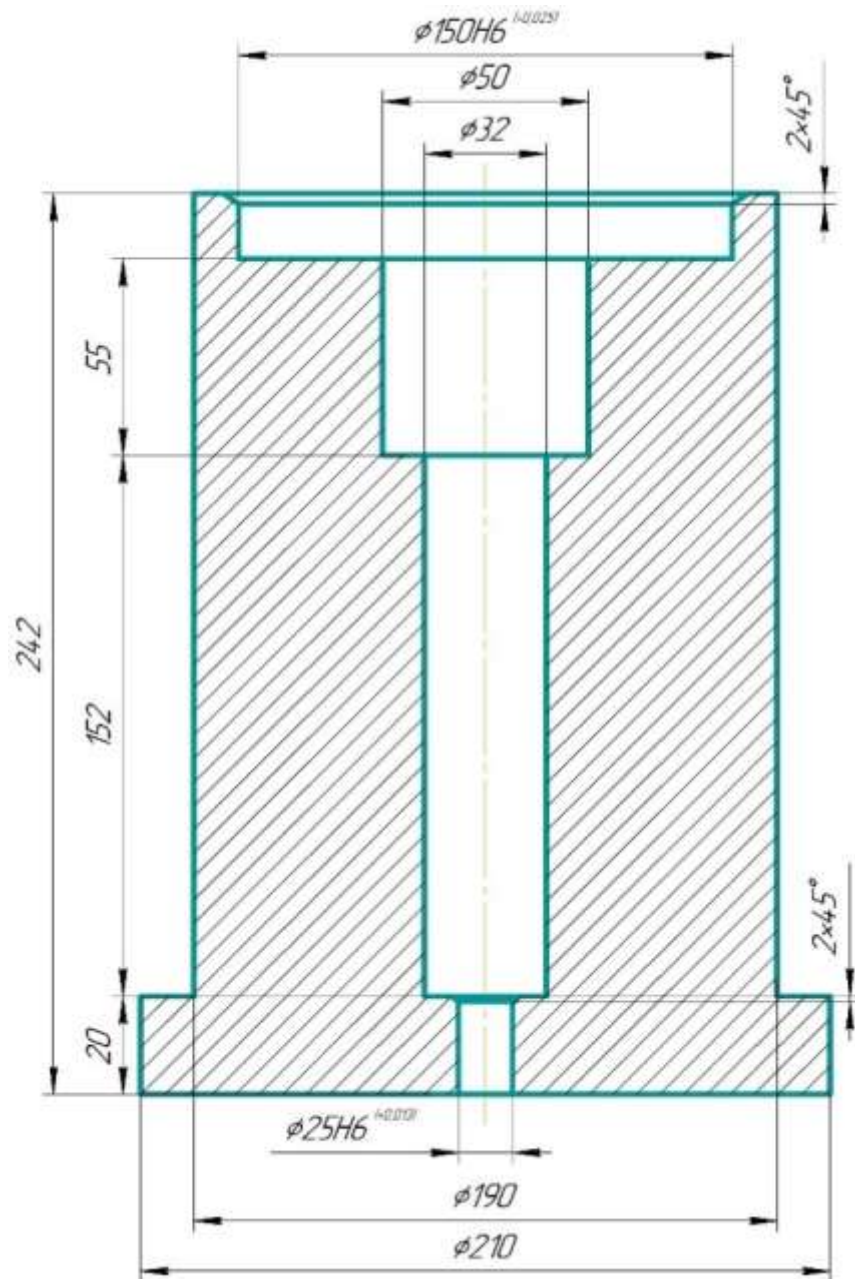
Центрирующее приспособление для сборки деталей клеевого соединения «первичный вал-подшипник» коробки передач КАМАЗ-4310
